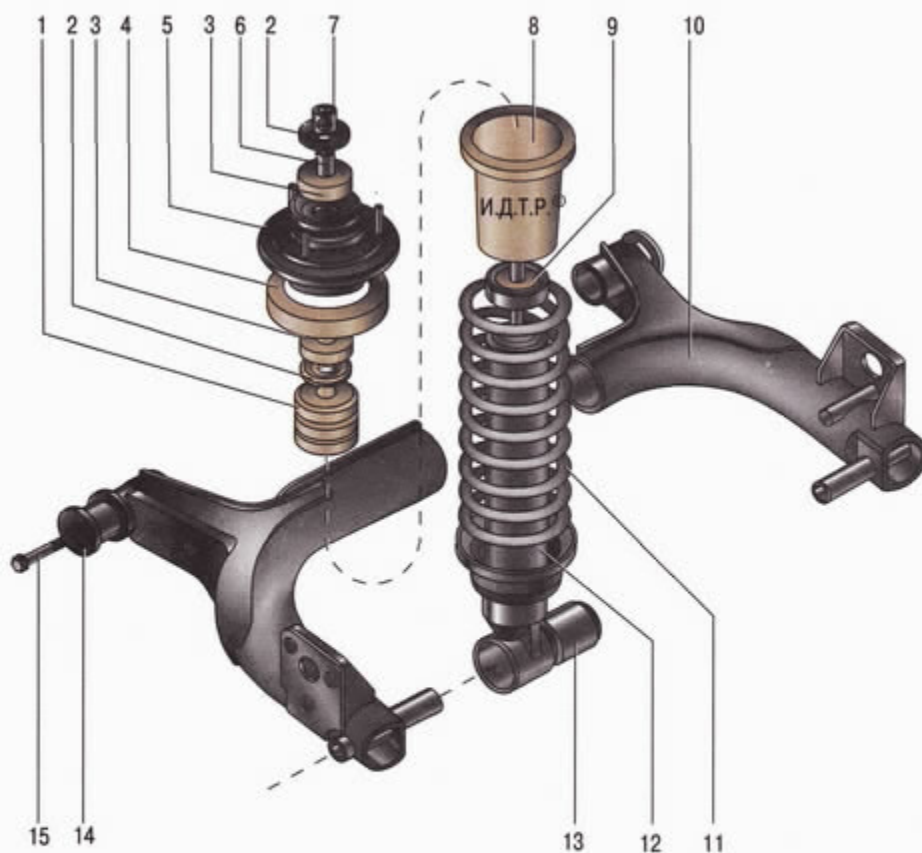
Детали задней подвески: 1 – буфер сжатия; 2 – обойма; 3 – подушка амортизатора; 4 – изоляционная прокладка пружины задней подвески; 5 – верхняя опора амортизаторной стойки; 6 – распорная втулка; 7 – гайка штока амортизатора; 8 – чехол; 9 – обойма буфера; 10 – балка задней подвески; 11 – пружина задней подвески; 12 – амортизатор; 13 – сайлентблок амортизаторной стойки; 14 – сайлентблок балки задней подвески; 15 – болт крепления балки задней подвески
